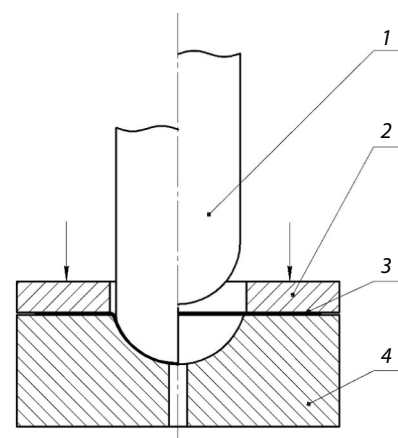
Схема вытяжки-штамповки в жестком штампе: 1 — пуансон; 2 — прижим; 3 — заготовка; 4 — матрица
